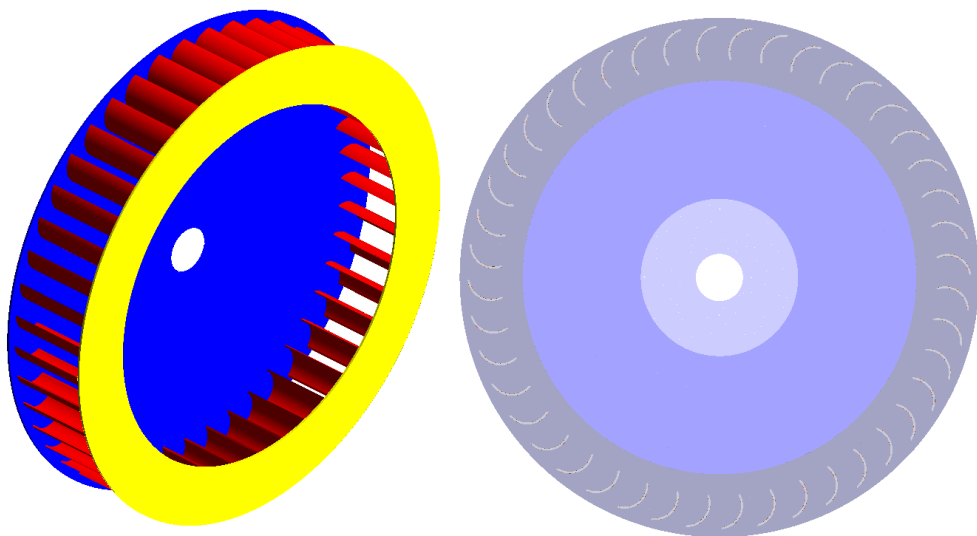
Geometria 3D do rotor Comercial de 330 mm de diâmetro
